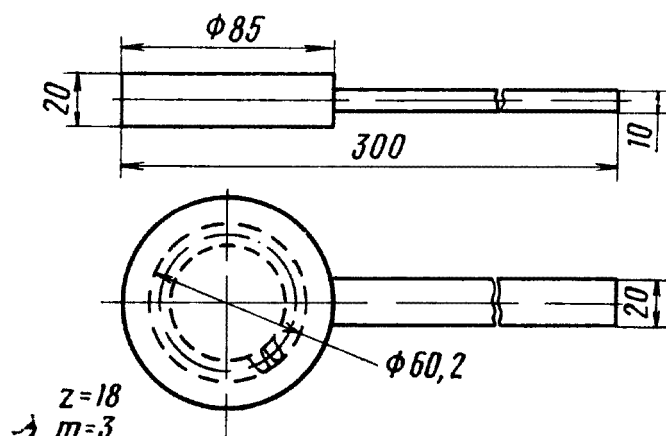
Приспособление для закрепления шестерни привода насоса рулевого управления
